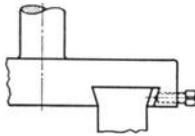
Befestigung eines Stempelfußes durch Schräge und Druckschraube.
